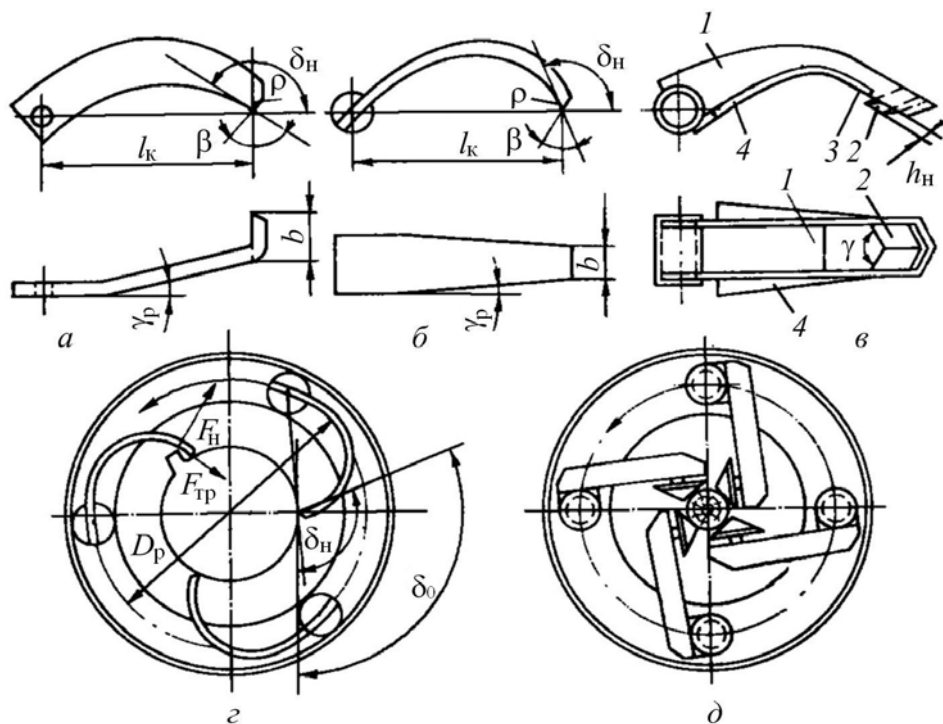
Окорочный инструмент роторных окорочных станков: а, б – скребковый окорочный инструмент; в – ножевой окорочный инструмент; г – схема взаимодействия короснимателя с остатками сучьев; д – схема установки конических фрез на роторе станка
